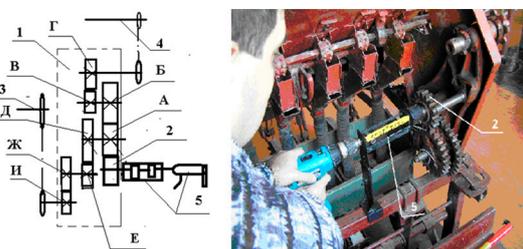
Схема присоединения устройства к редуктору сеялки: 1 – редуктор зерновой сеялки; 2 – зубчатка устройства; 3 – вал зерновых аппаратов; 4 – вал туковывсевающих аппаратов; 5 – разработанное устройство привода; А – зубчатка редуктора, установленная на его первичном вале
